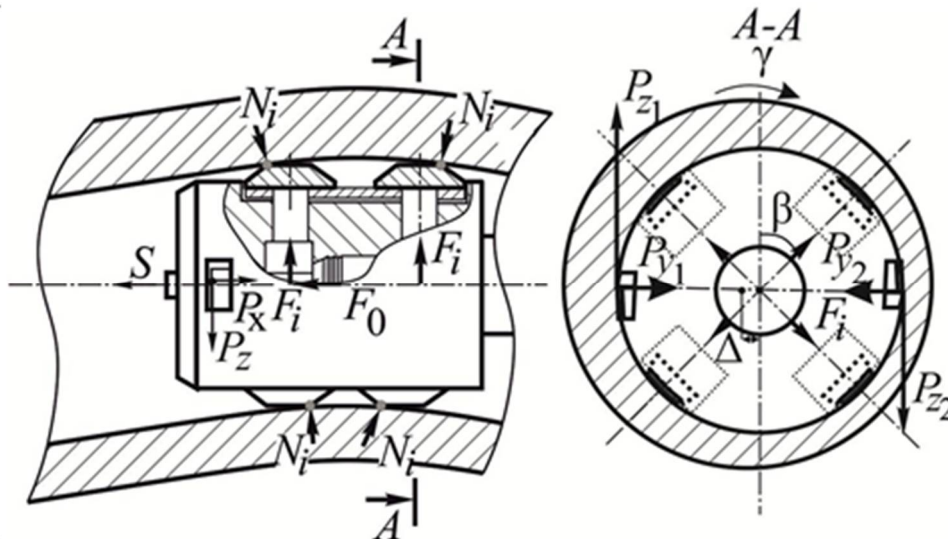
Сили і моменти, що діють на розточувальних головку при обертанні заготовки
